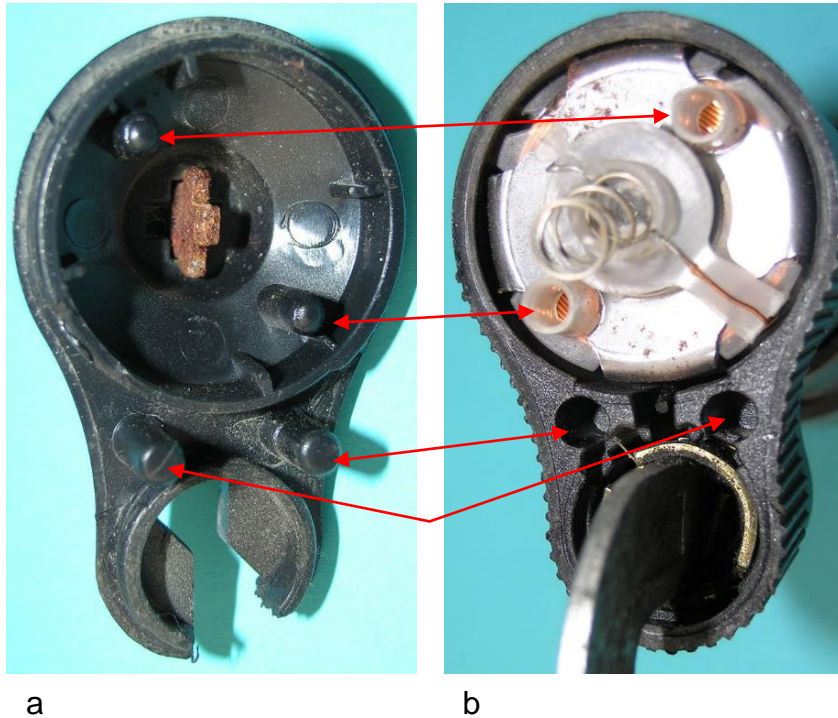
Kraftschlüssige Befestigung des Bodens mit vier Zapfen:
